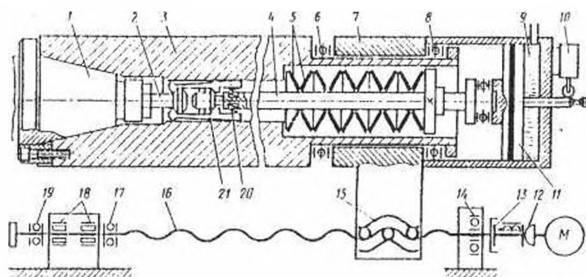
Схема механізму автоматичного кріплення інструмента і рушія подач:
